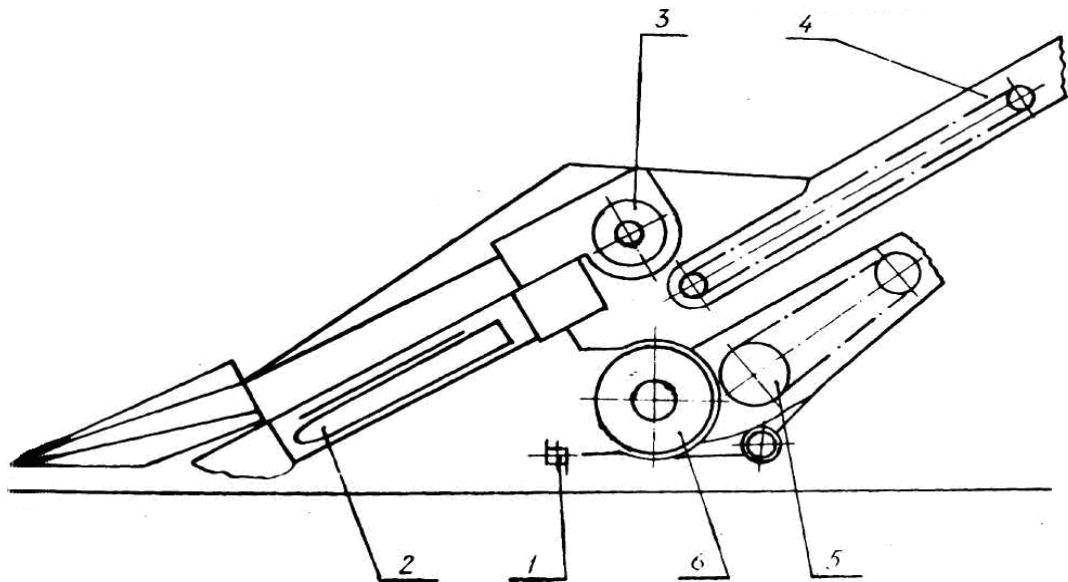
Схема жатки 3-го виду: 1- різальний механізм; 2 –качано-відокремлювальний механізм; 3 - качано напрямний шнек; 4,5 - елеватор; 6-стебловий шнек
